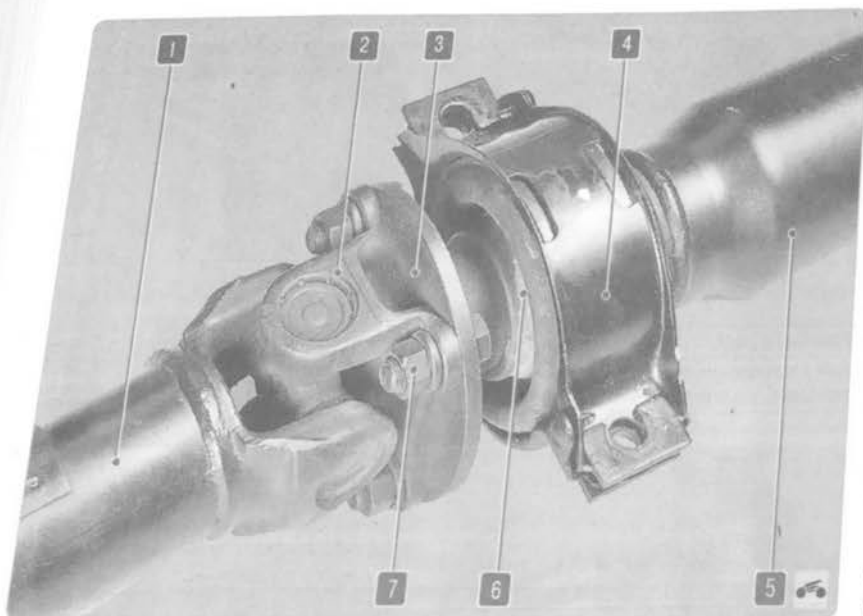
Промежуточная опора задней карданной передачи: 1 – задний вал; 2 – вилка фланца заднего вала; 3 – задний фланец промежуточного вала; 4 – корпус опоры; 5 – промежуточный вал; 6 – резиновый демпфер; 7 – гайка крепления фланца вилки
